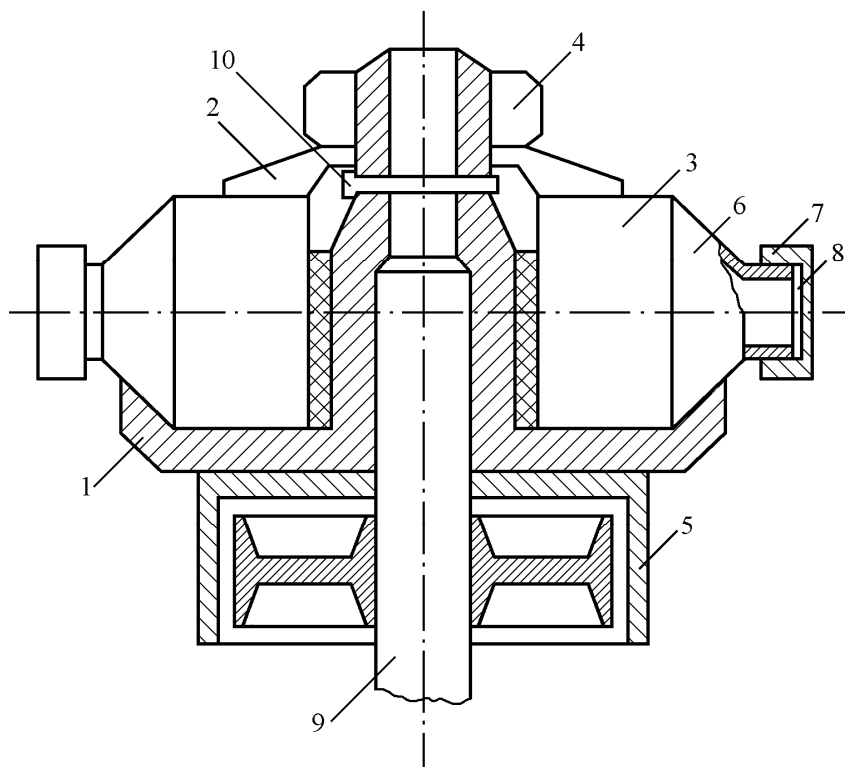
Конструкция ротора центрифуги: 1 – основание; 2 – фланец крепления; 3 – стакан; 4 – гайка накидная; 5 – тормозной диск; 6 – горловина стакана; 7 – заглушка; 8 – съемная мембрана; 9 – вал двигателя; 10 – палец
